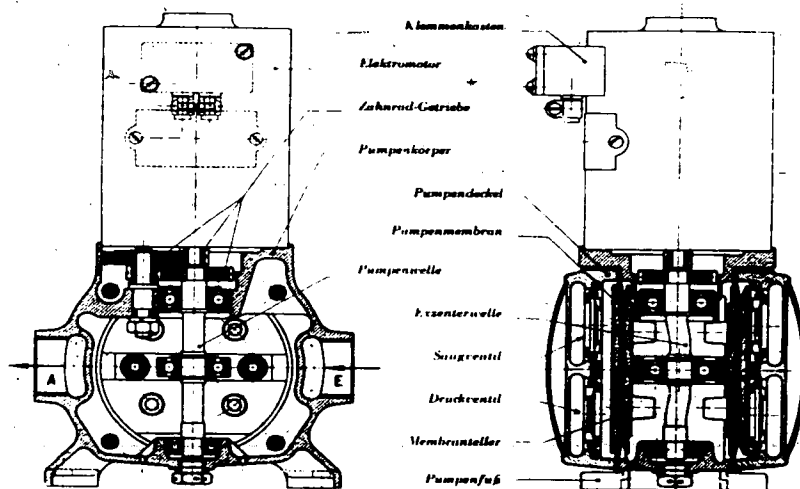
Doppel-Membranpumpe mit angeflanschem El.-Motor DBU-UP 1. Schnitt
